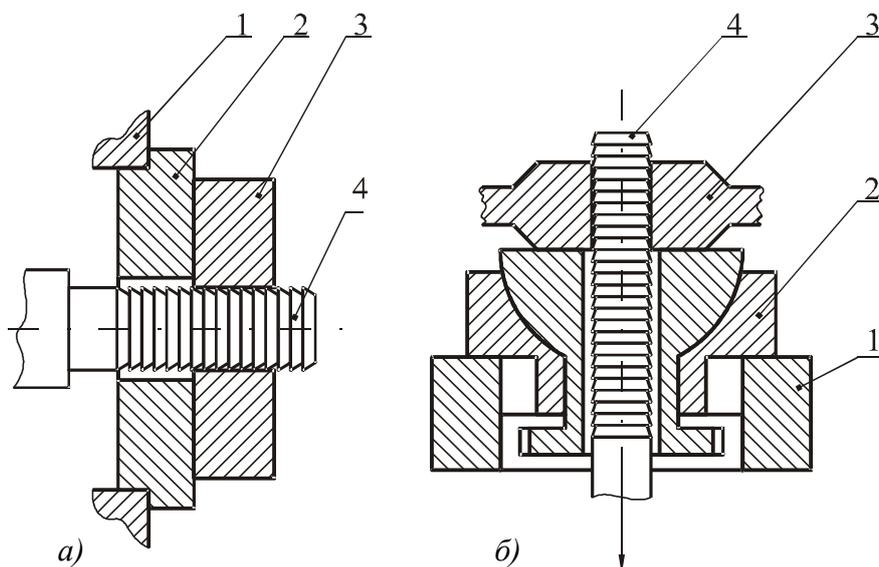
Схемы протягивания отверстий: *а* – горизонтальная; *б* – вертикальная; 1 – жесткая опора; 2 – шаровая опора; 3 – обрабатываемая заготовка; 4 – протяжка
